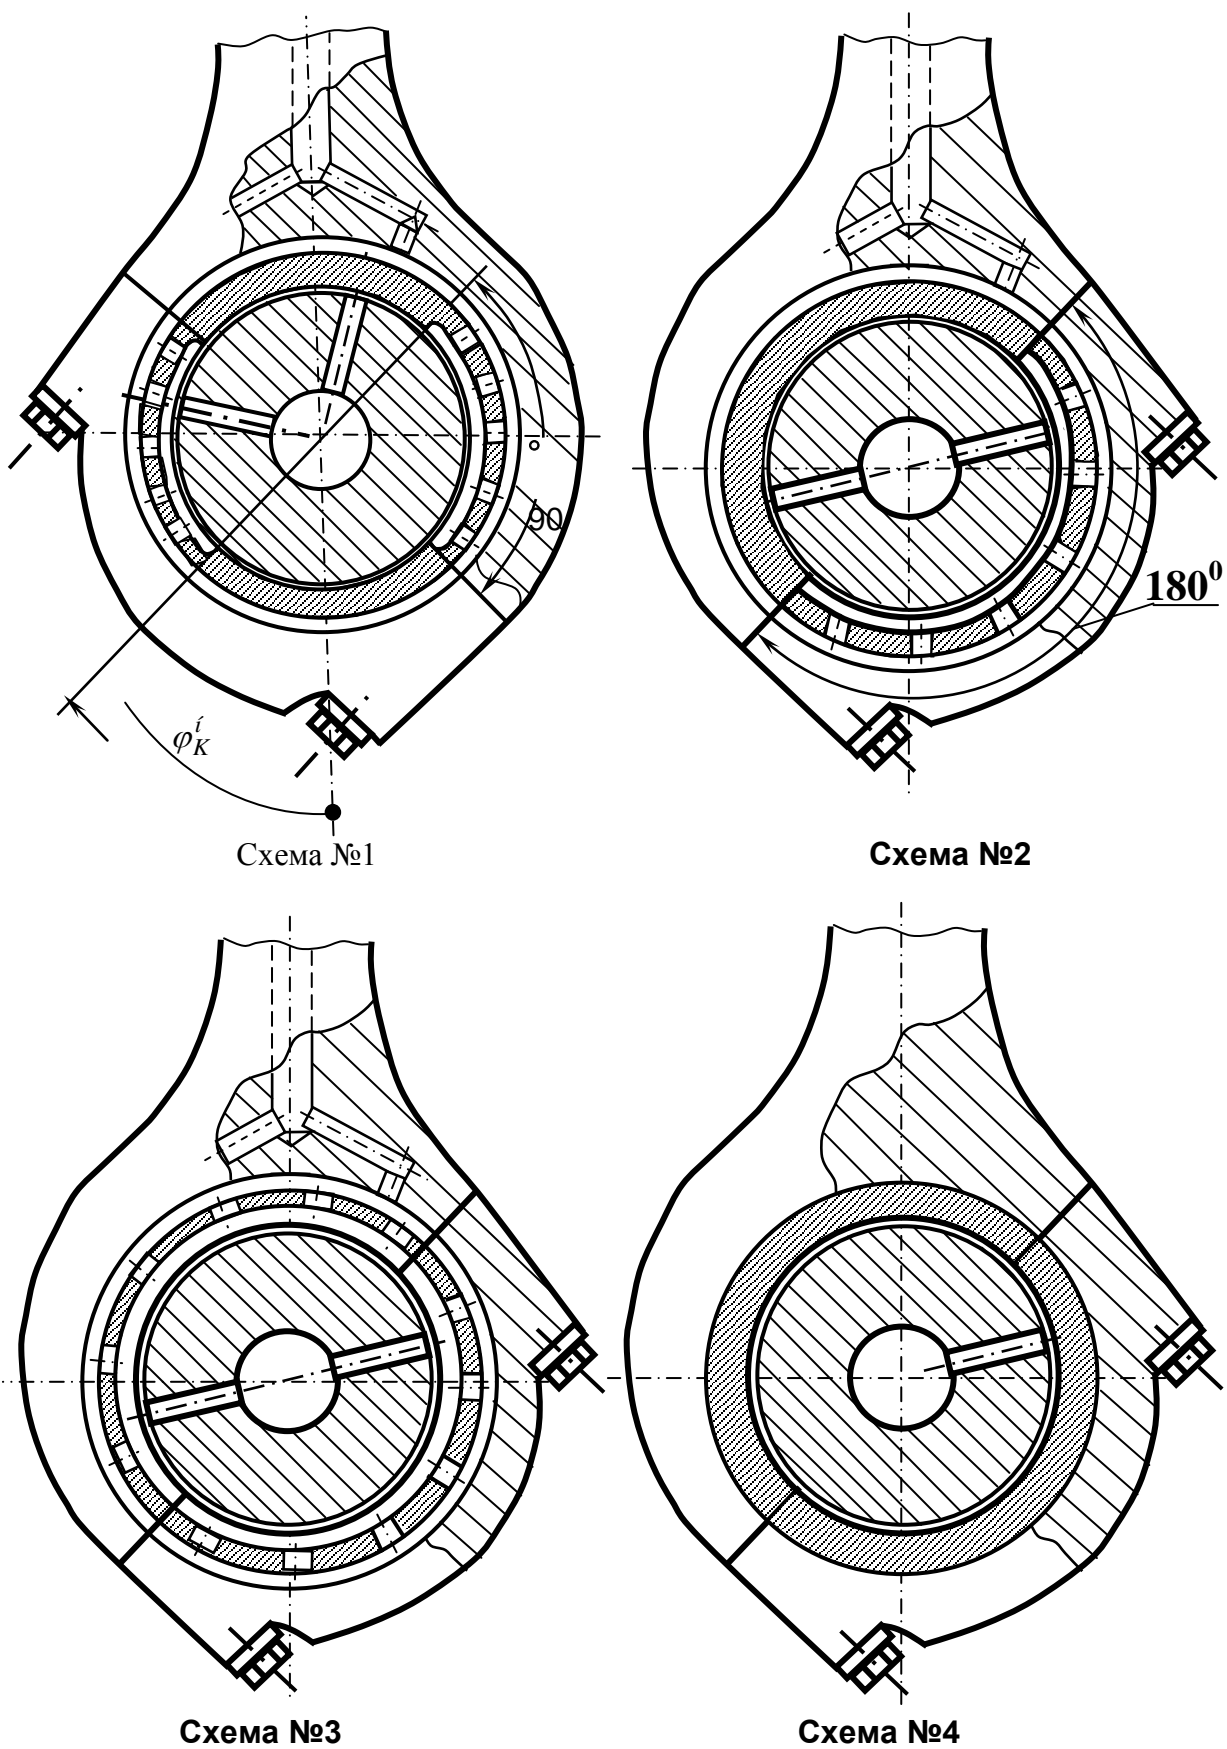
Возможные схемы подачи смазки в шатунный подшипник двигателя ДМ-21
